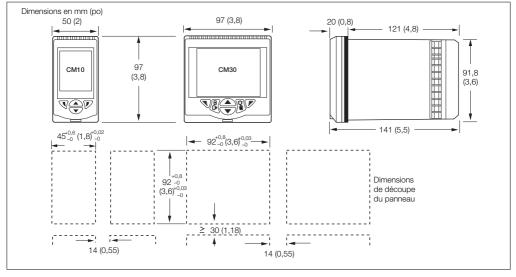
Dimensions des ControlMaster CM10 et CM30
